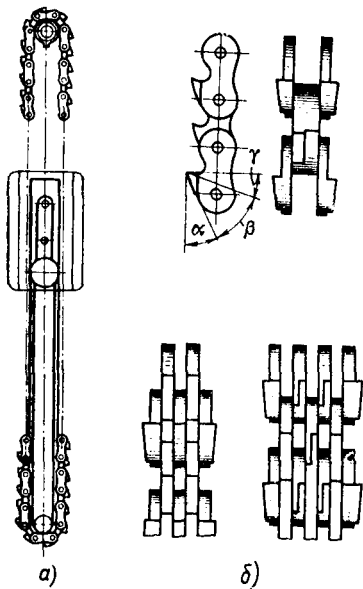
Режущая (фрезерная) цепочка для цепнодолбежного станка:
